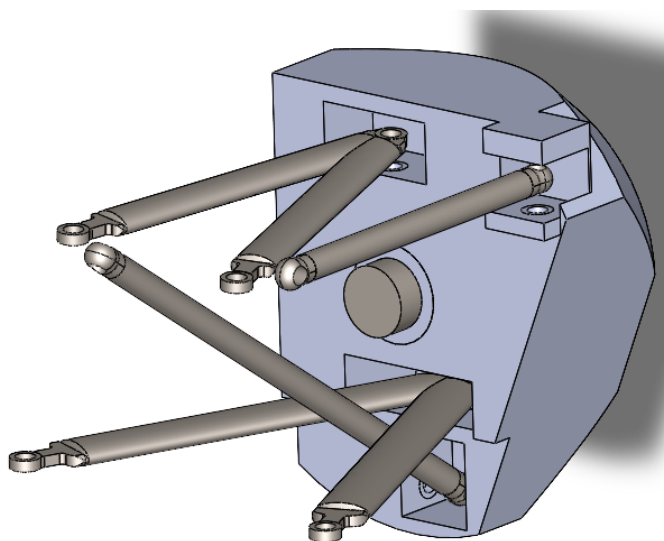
Conjunto completo com a remoção de material visível (1).
